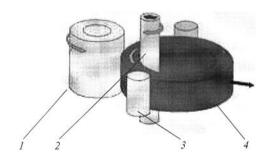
Радиальная кольцераскатка: I — главный валок; 2 — дорновой валок; 3 — центрирующий валок; 4 — кольцо
